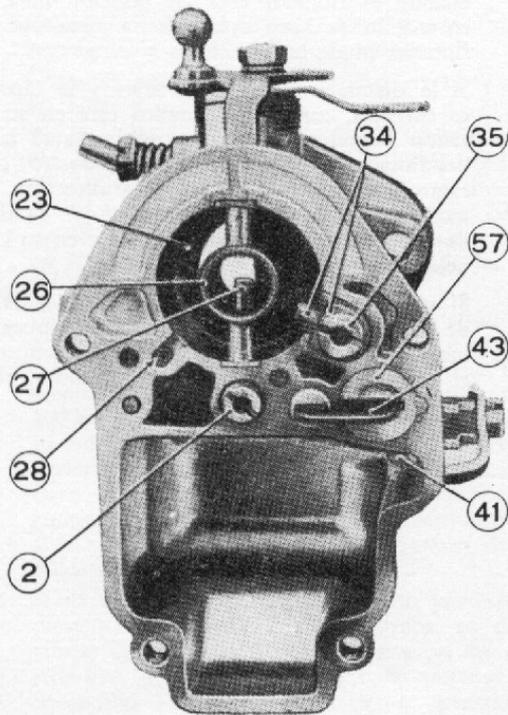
Cuerpo del carburador con la tapa quitada.
